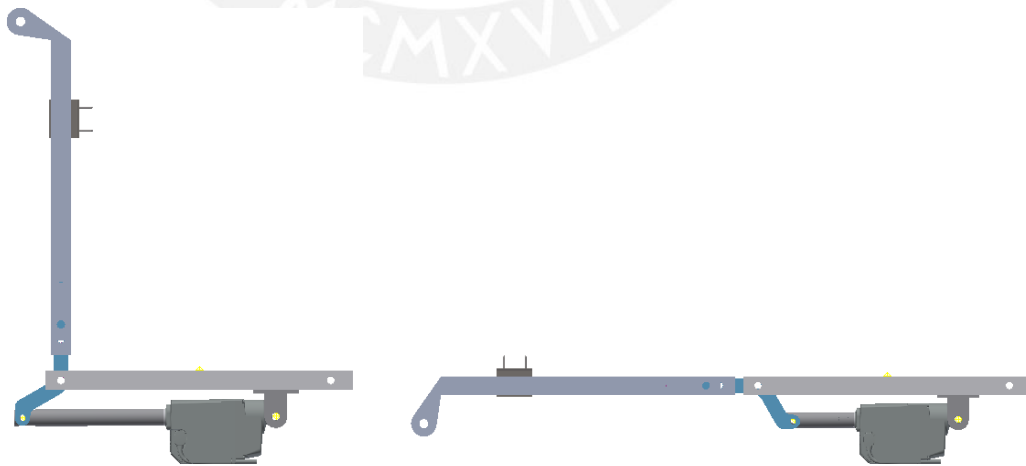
Giro del espaldar - Vista frontal de la posición inicial y final
